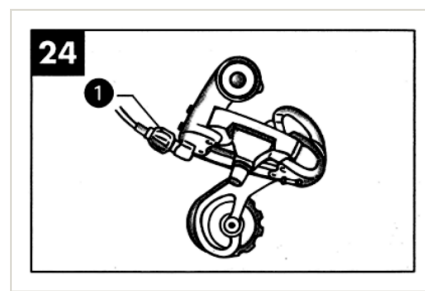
Dérailleur arrière indexé : 1 vis de réglage
